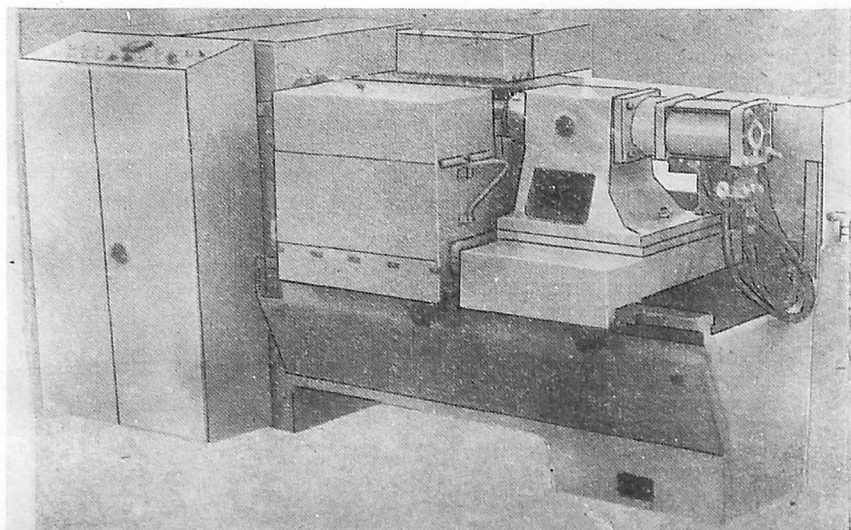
Общий вид станка мод. МАС-4 для обработки крупногабаритных цилиндров автомобиля
